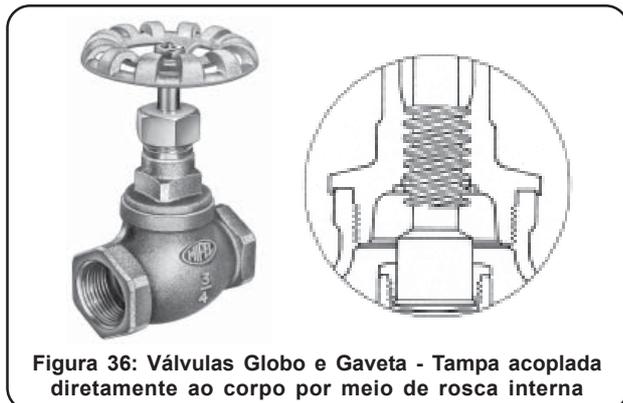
Válvulas Globo e Gaveta - Tampa acoplada diretamente ao corpo por meio de rosca interna
